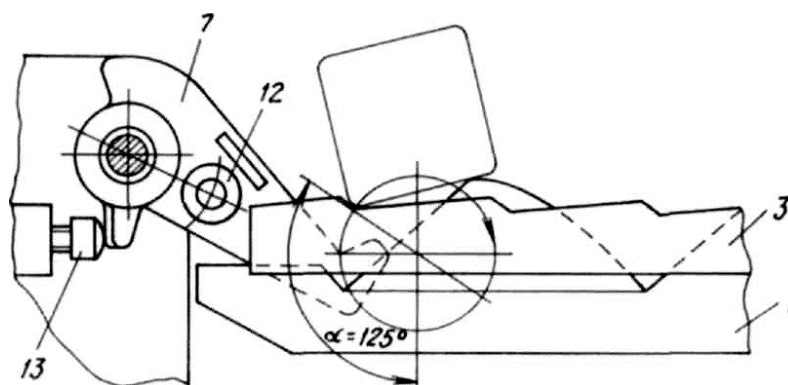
Механізм у момент захоплення заготівлі транспортними рейками [6]
